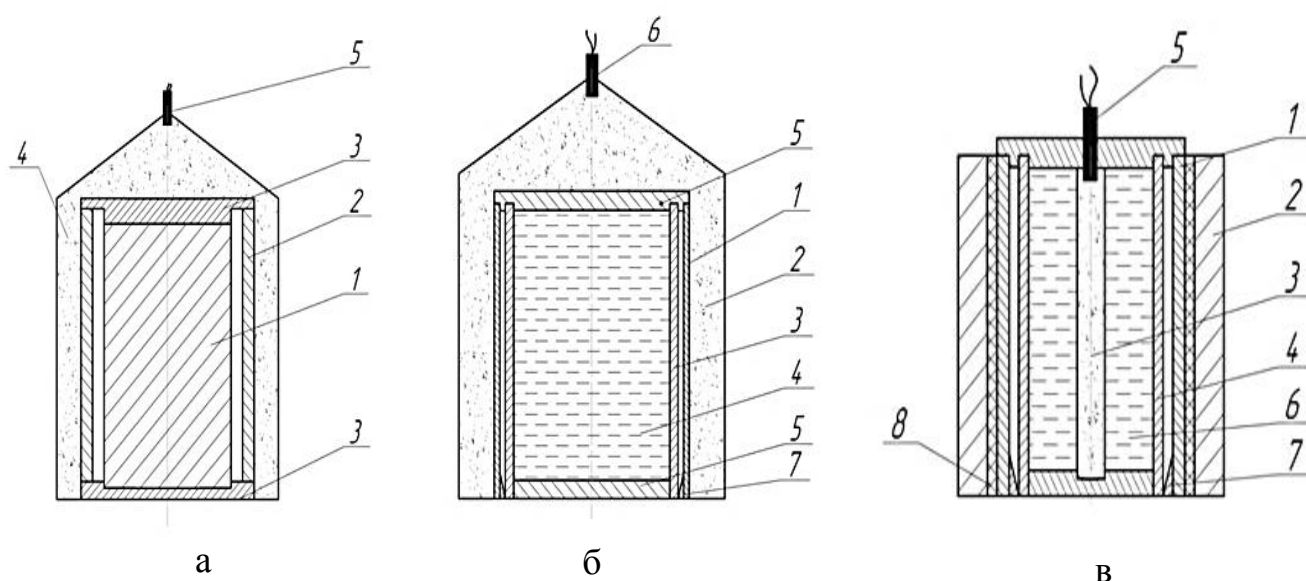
Схемы плакирования взрывом труб и стержней: а – плакирование стержня (1 – стержень, 2 – наружная труба, 3 – центровочные крышки, 4 – ВВ, 5 – детонатор); б – плакирование труб наружным зарядом ВВ (1 – наружная труба, 2 – ВВ, 3 – внутренняя труба, 4 – наполнитель, 5 – центровочные крышки, 6 – детонатор, 7 – центровочное кольцо); в – плакирование с использованием передаточной среды (1 – наружная труба, 2 – матрица, 3 – детонационный шнур, 4 – внутренняя труба, 5 – детонатор, 6 – наполнитель, 7 – центровочное кольцо, 8 – демпфирующий слой).
